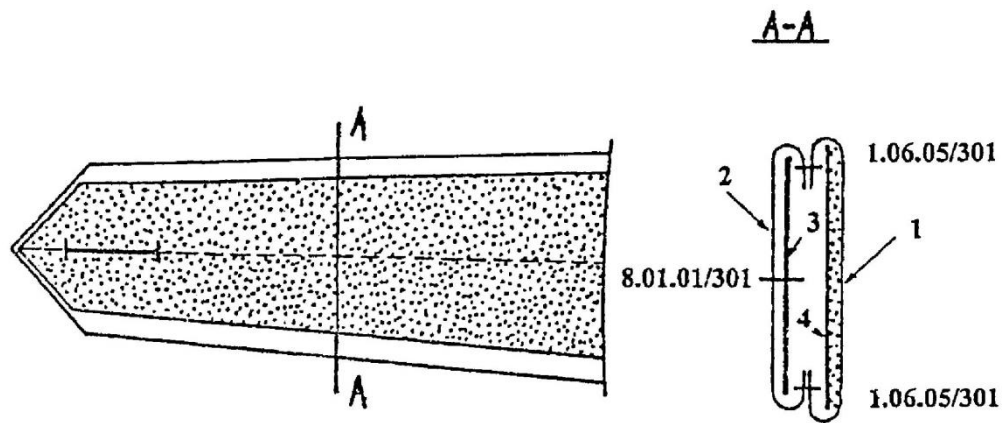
Klejenie rękawów wierzchnich i boczku
